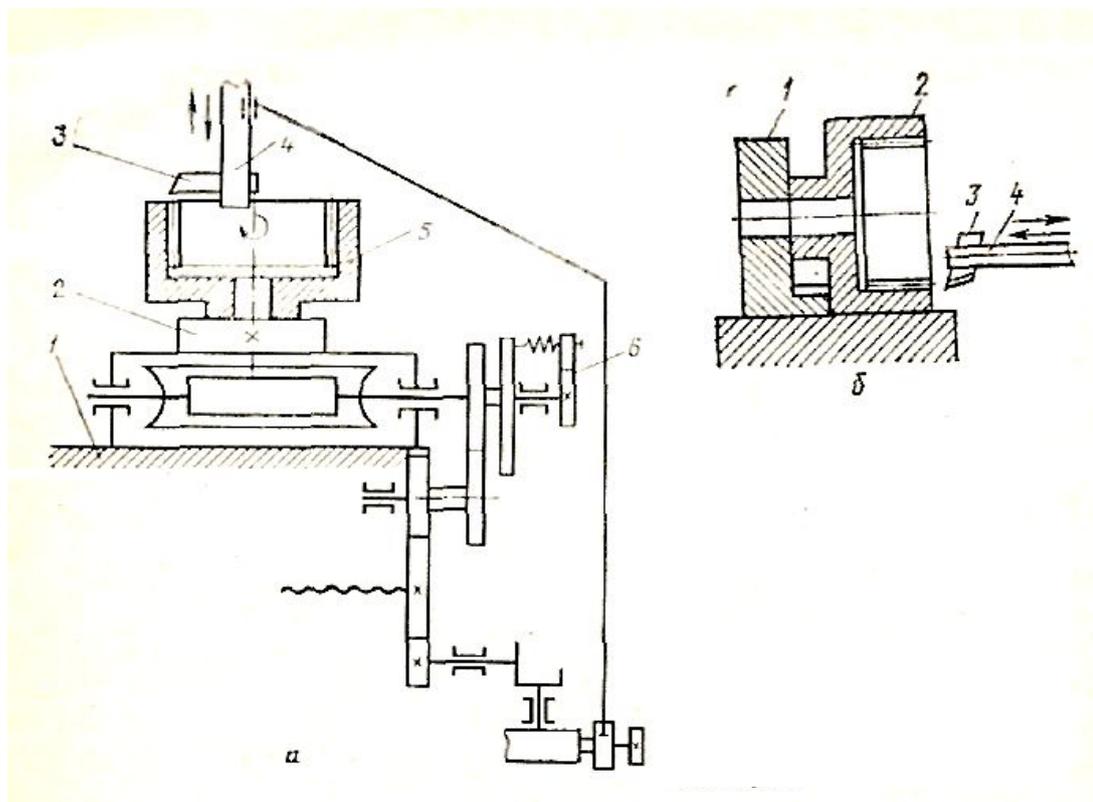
Приспособления для обработки зубьев ремонтируемой тарельчатой шестерни.
